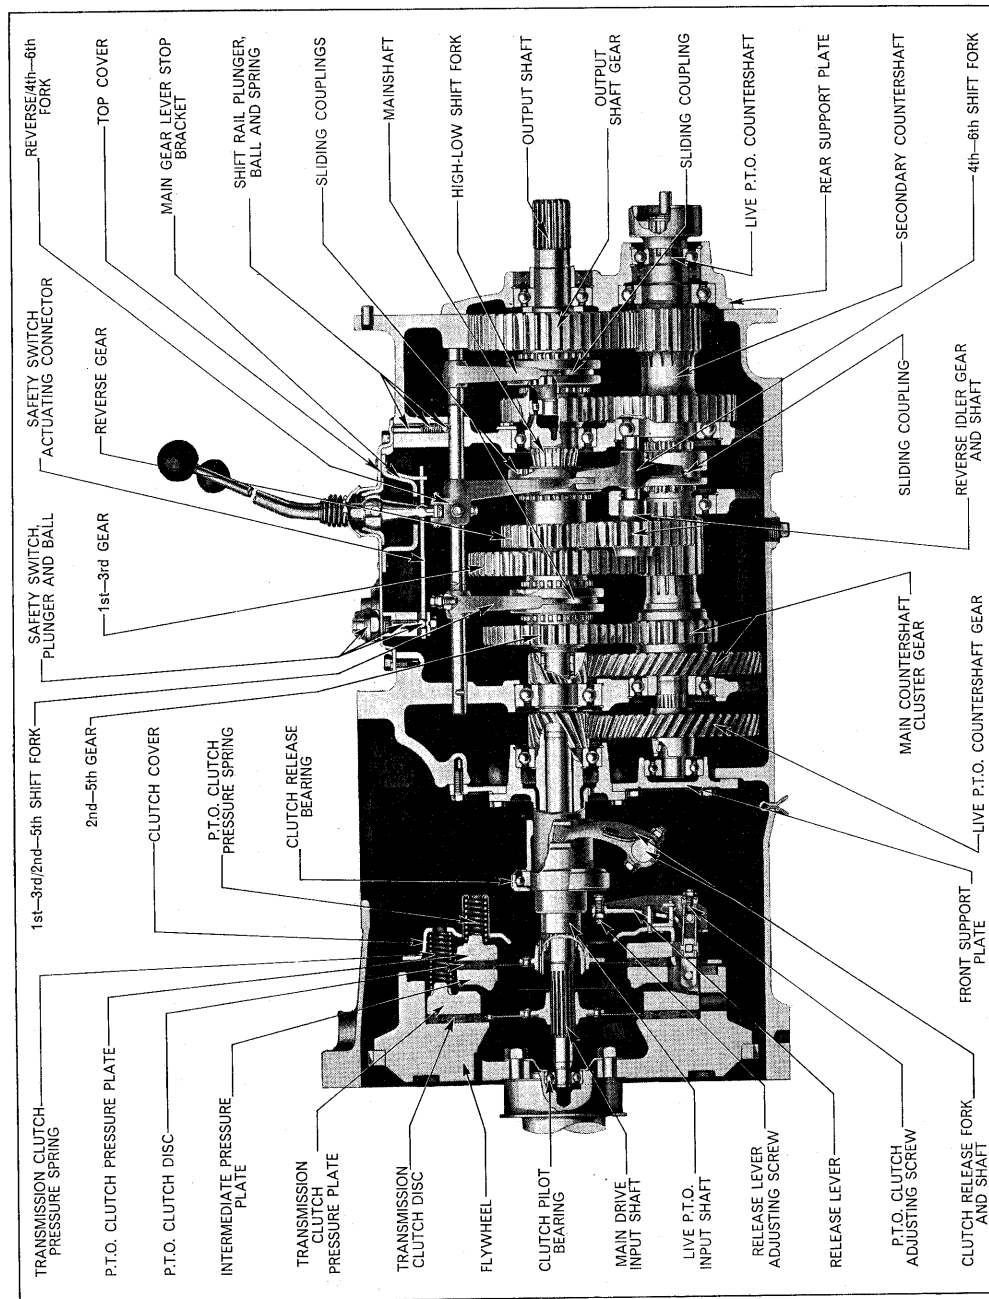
Gearkasse og reduktionsgearkasse (her med dobbeltkobling).
